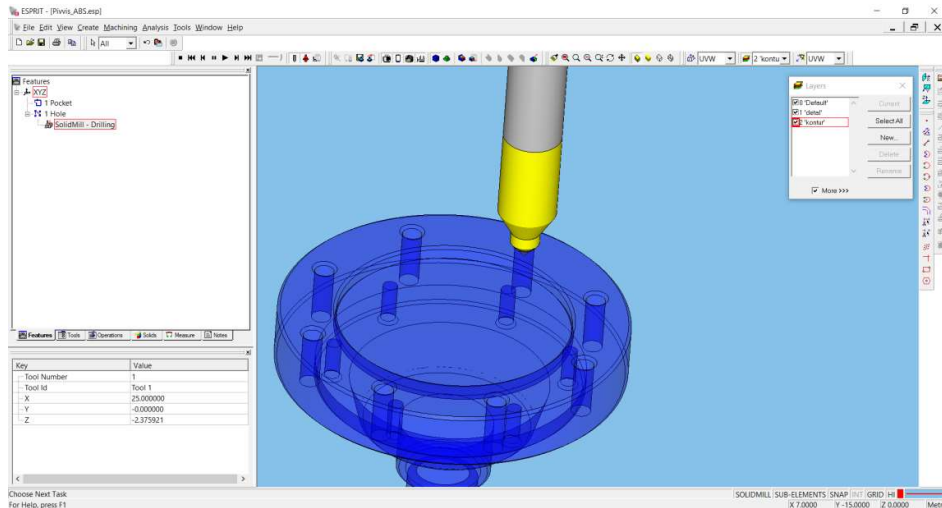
Траєкторія руху металорізального інструменту при обробленні кришки
